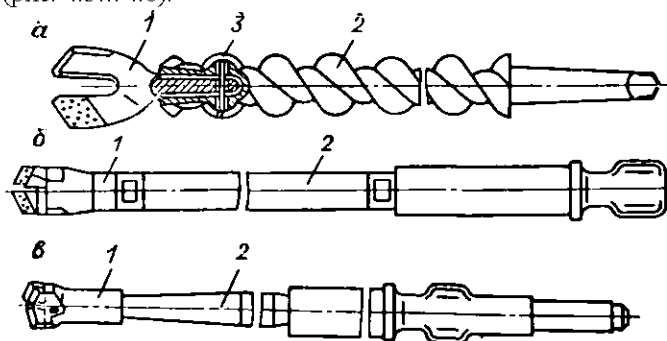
Инструмент для вращательного бурения: 1 – резец; 2 – буровая штанга; 3 – соединительный шплинт.
